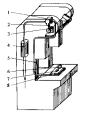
气吹出件装置 1一气阀; 2一阀杆; 3一凸轮; 4一储气筒; 5一管道; 6一工件; 7一下模; 8一喷嘴
